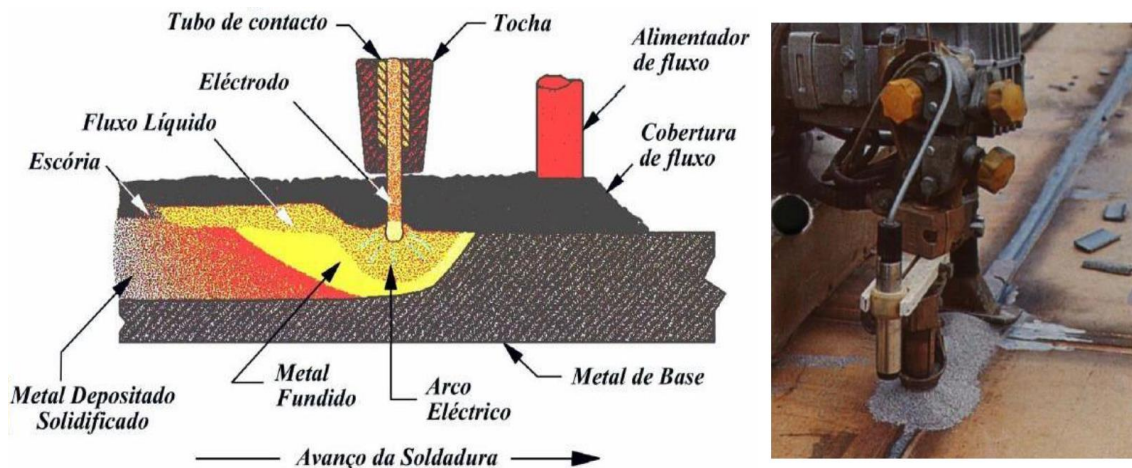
Esquema soldadura arco submerso [21]
